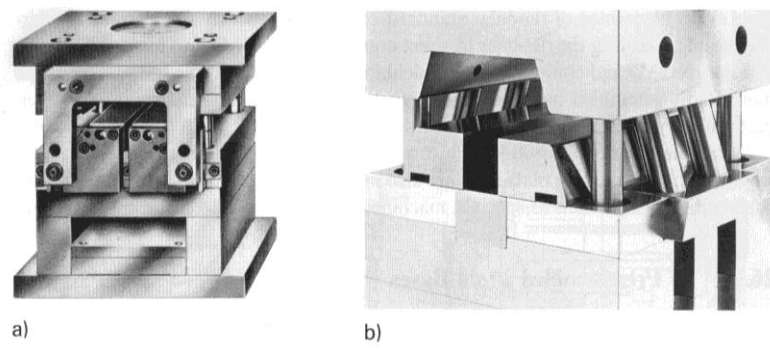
(a) Molde seccionado, actuado por deslizadores; (b) Molde Seccionado actuado con deslizadores en ángulo.
